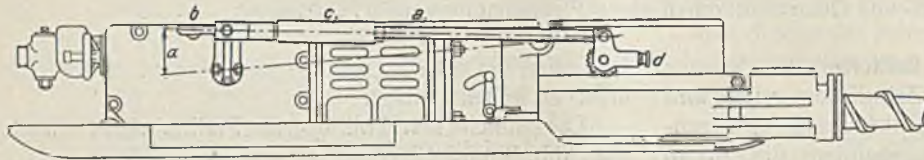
Einrichtung zum maschinenmäßigen Schwenken der Schrämmaschine (Eickhoff).
